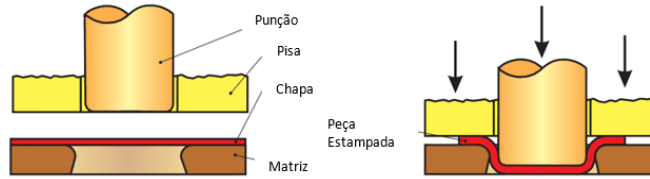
Estampagem Profunda Singular (Schuler GmbH)
